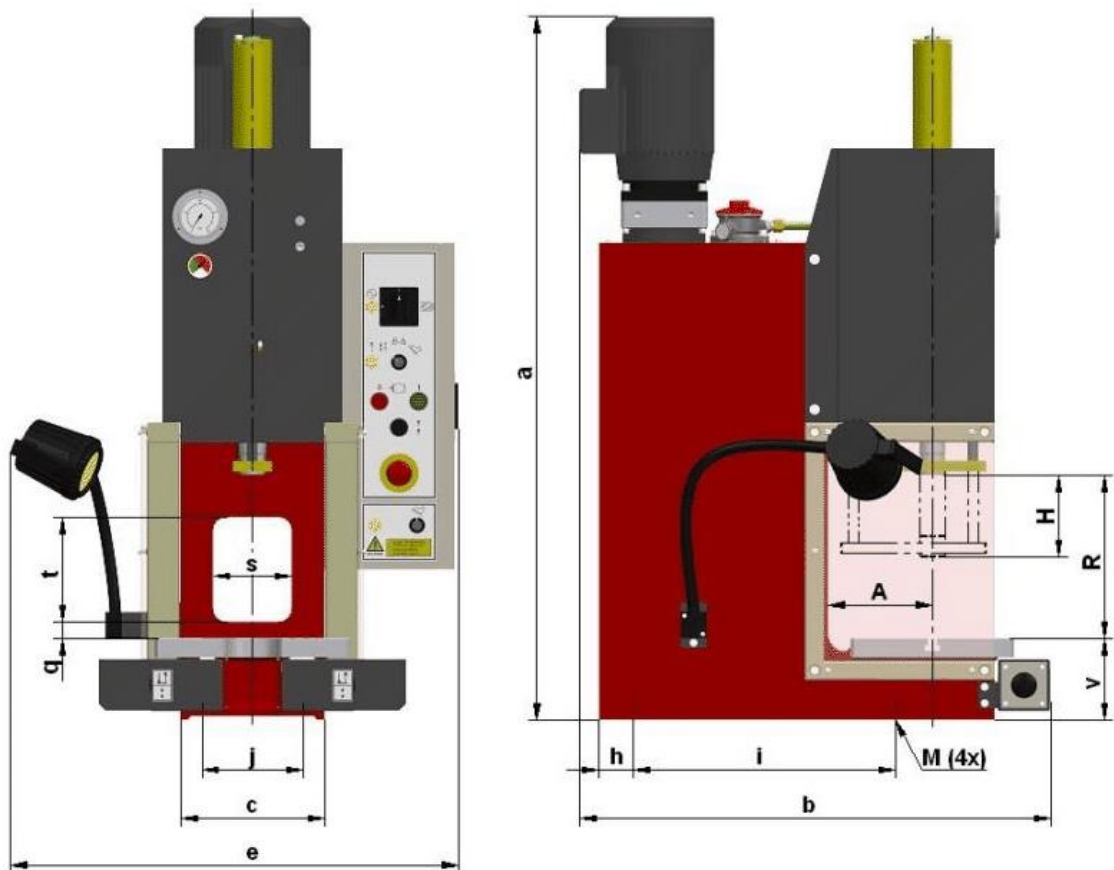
Stolní hydraulický lis HOLZMANN WP 10 H.
